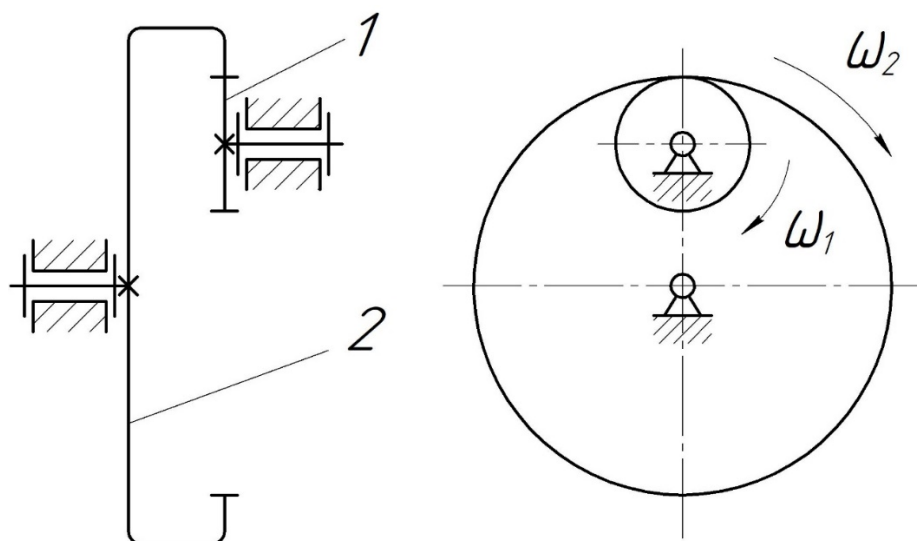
Схема цилиндрической зубчатой передачи внутреннего зацепления
